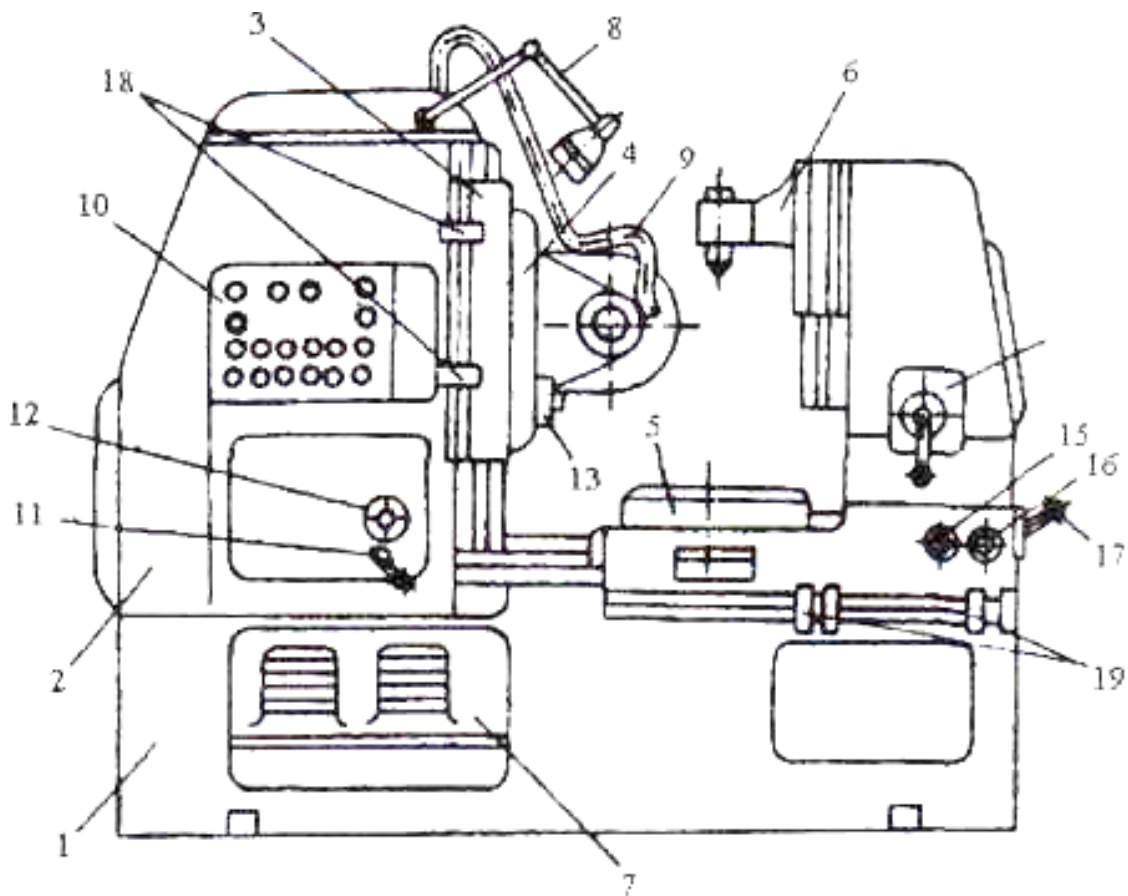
Загальний вигляд зубофрезерного верстата моделі 5K324А
